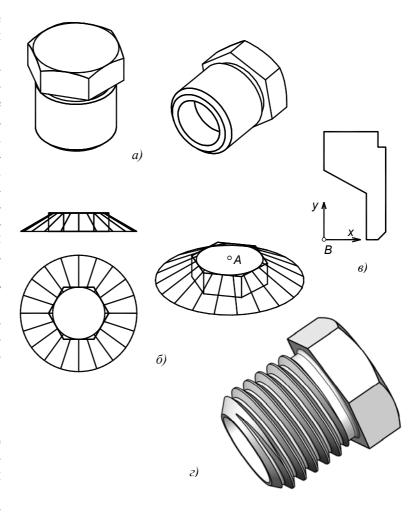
Построение модели пробки: a — форма пробки; δ — построение шестигранной головки; δ — контур вращения; ϵ — пробка с резьбой
